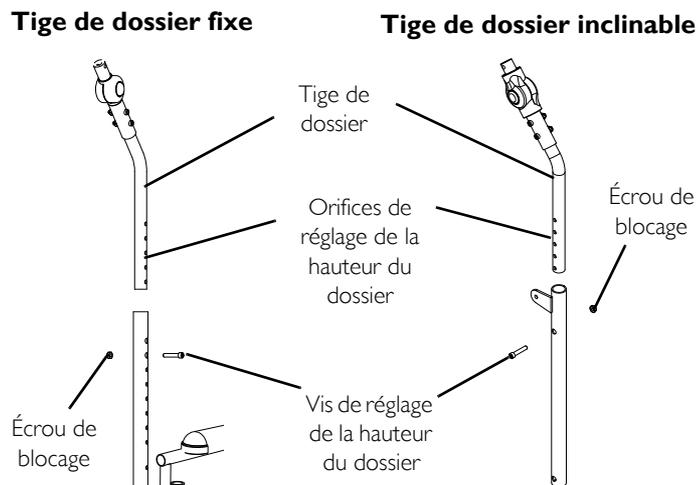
FIGURE I Réglage de la hauteur des tiges de dossier réglables
